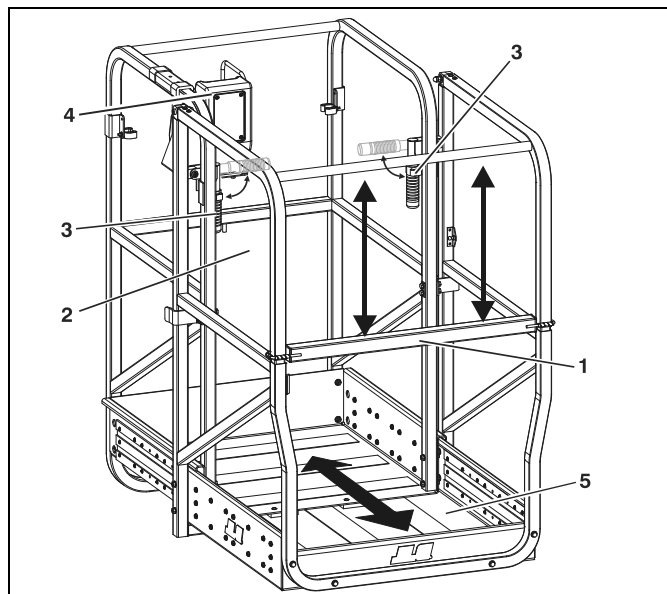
PLATE-FORME EXTENSIBLE (ACCÈS À BARRE COULISSANTE À L'AVANT - CE)
